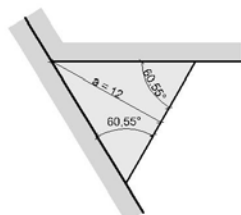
Untersuchte Schweißnahtgeometrien für a = 12mm
